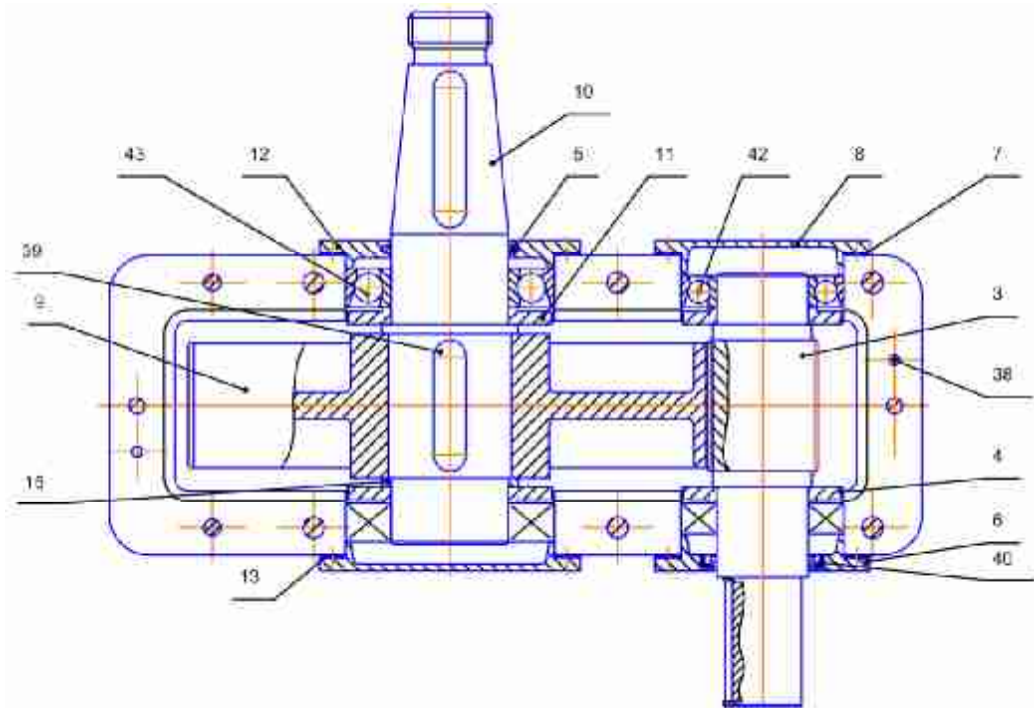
Одноступенчатый редуктор с цилиндрическими колесами:
